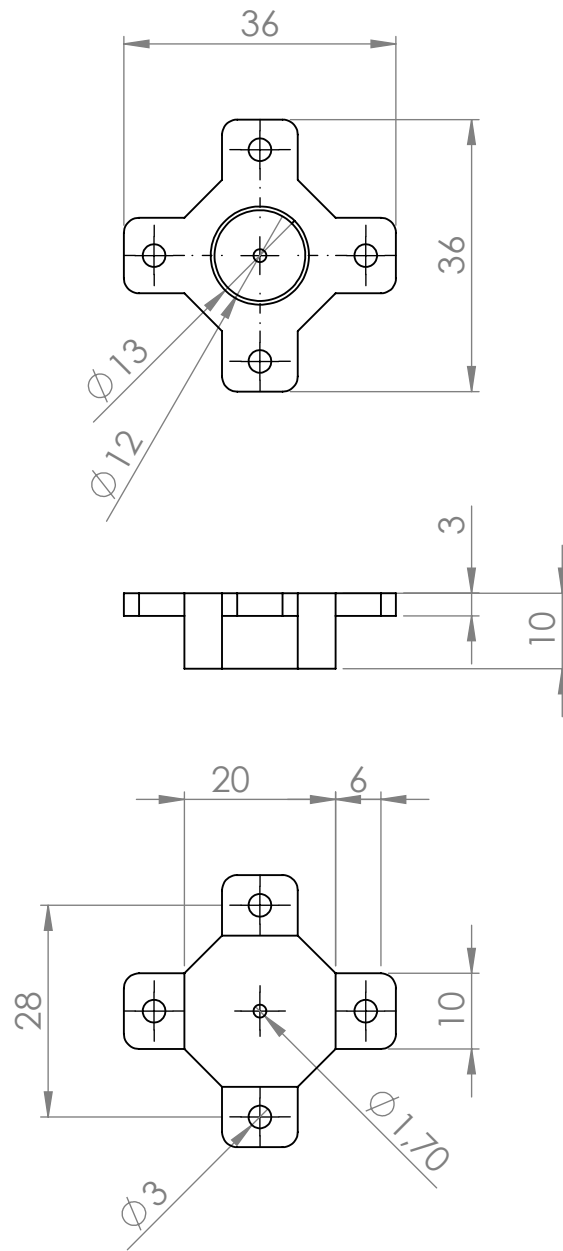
Diseño del molde para enmallado interno del *Robot Shear* parte A
